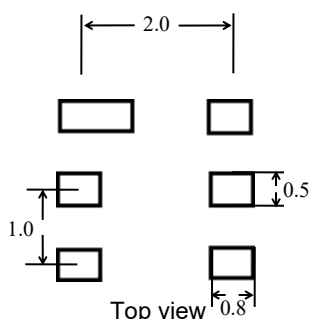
推荐WHT20B PCB设计尺寸（单位: mm）
